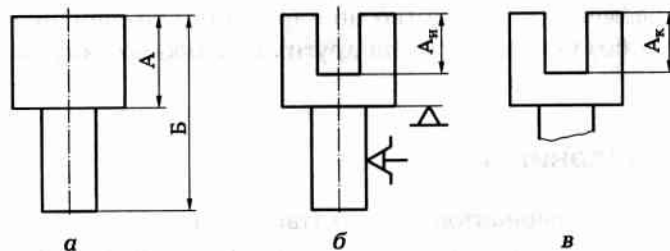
Схема получения паза: а — заготовка; б — исходный размер; в — конструкторский размер
